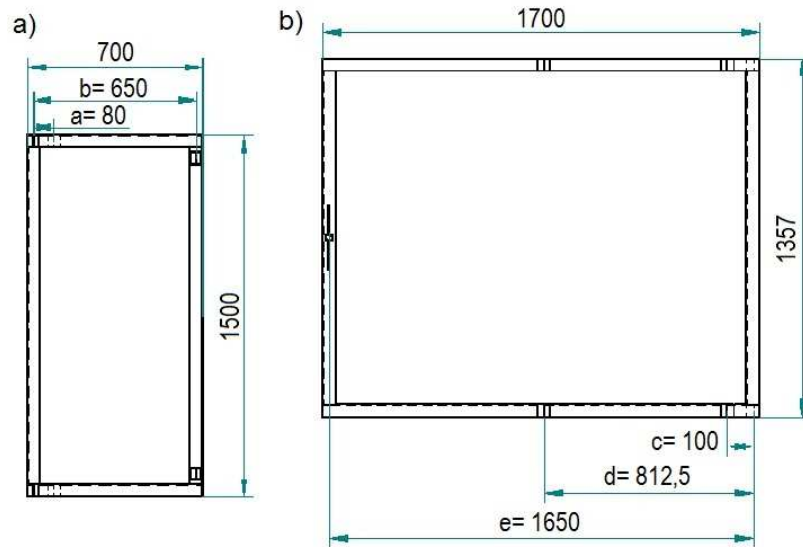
Widok elementów konstrukcyjnych wagi, rama – 1, rama główna – 2
